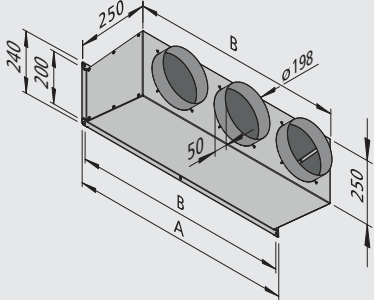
Disposizione schematica degli accessori in lamiera d'acciaio per il montaggio a soffitto
